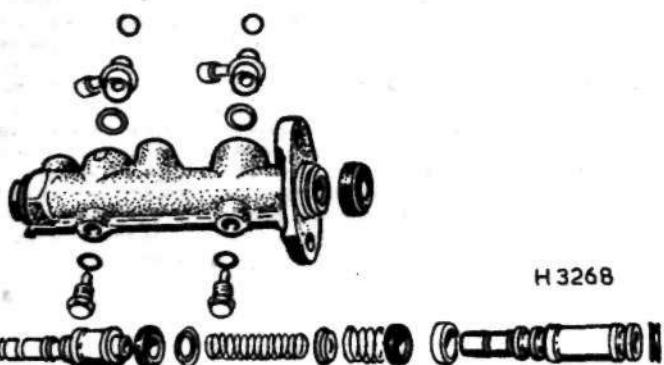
Детали главного тормозного цилиндра (Раздел 13)
